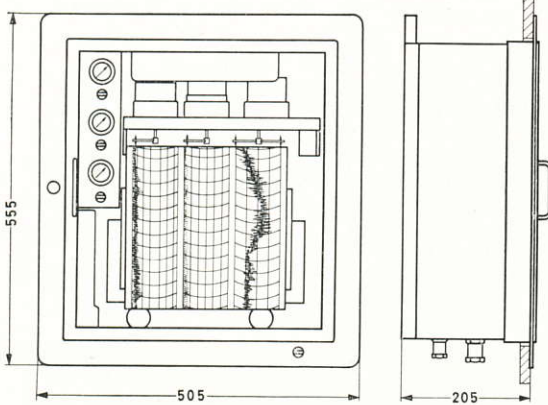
mit Gehäuse für versenkten Schalttafeleinbau 90zBS
